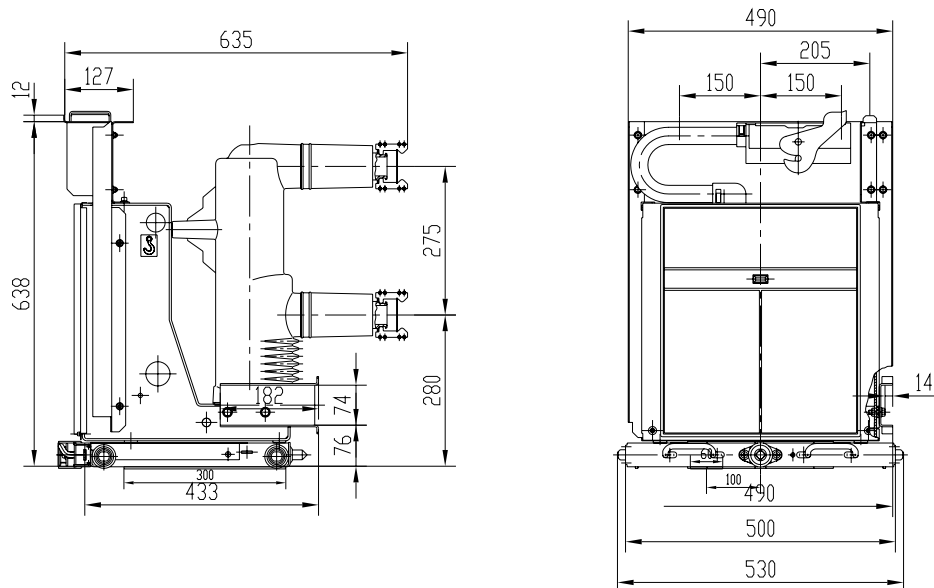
Габаритный размер выключателя ВВ-12 выкатного исполнения для ячейки шириной 800 мм
